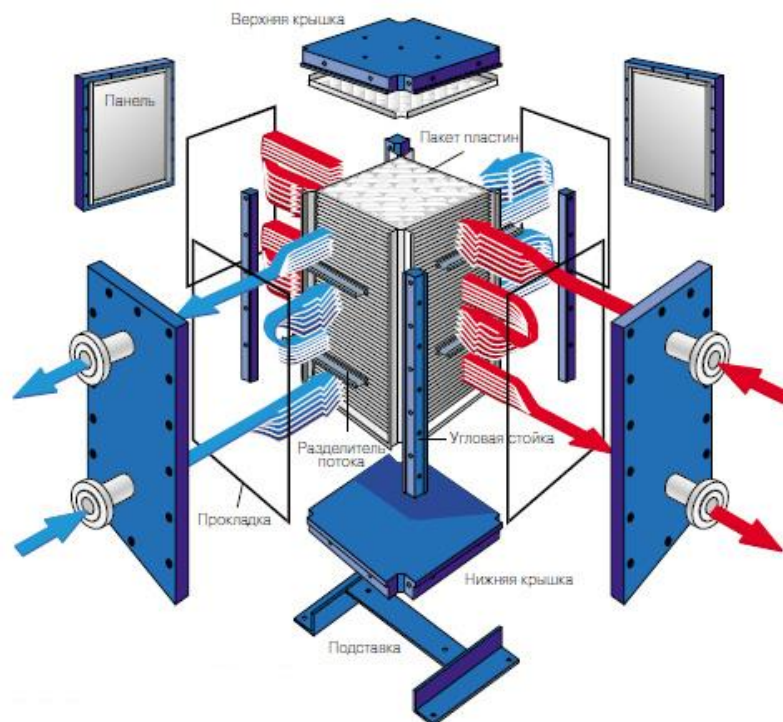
Конструкция сварного теплообменного аппарата
